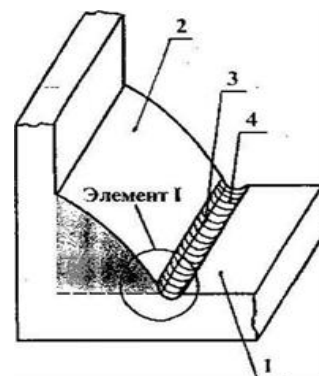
Типовая схема УУО с формированием «канавки»: 1 – основной металл; 2 – металл сварного шва; 3 – линия сплавления сварного шва с основным металлом; 4 – зона УУО («канавка»)
